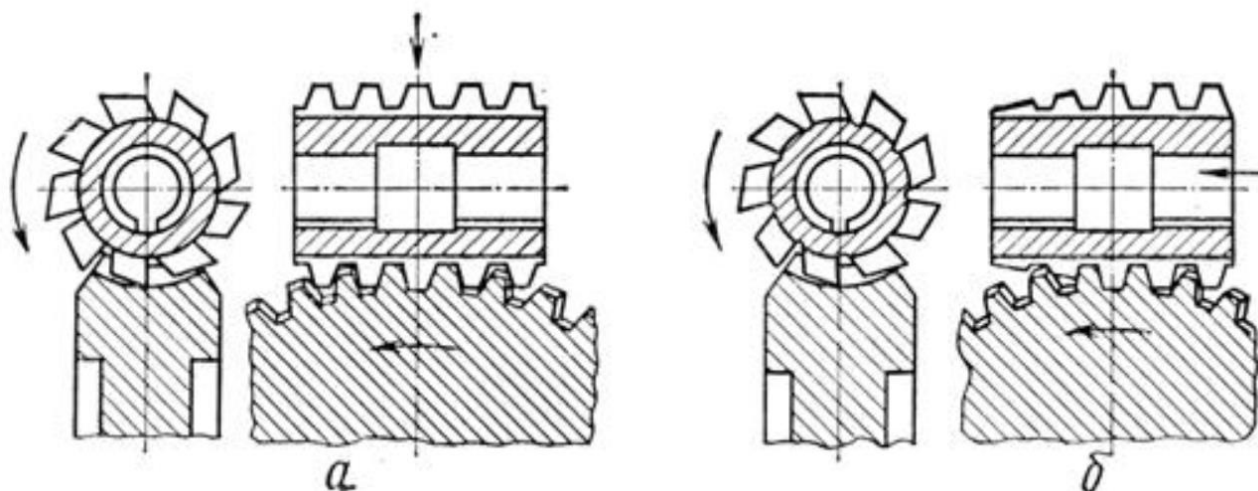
Фрезерування зубів черв'ячного колеса:
